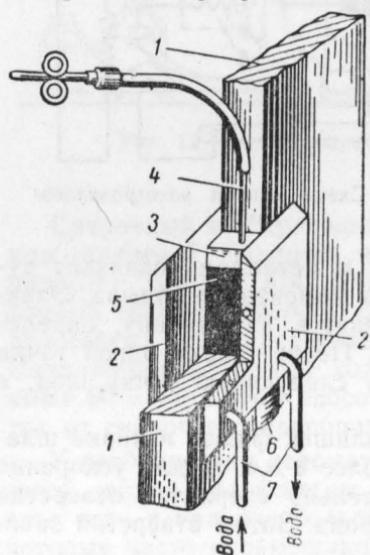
Схема процесса электрошлаковой сварки
